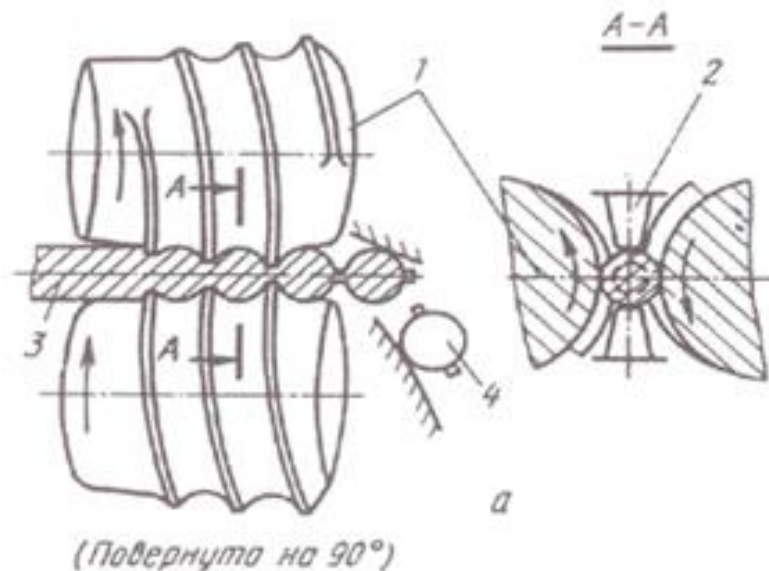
Схема розташування валків та проводок при прокаті куль: 1 - валки; 2 - напрямні лінійки; 3 - вихідна заготовка; 4 – заготовка
